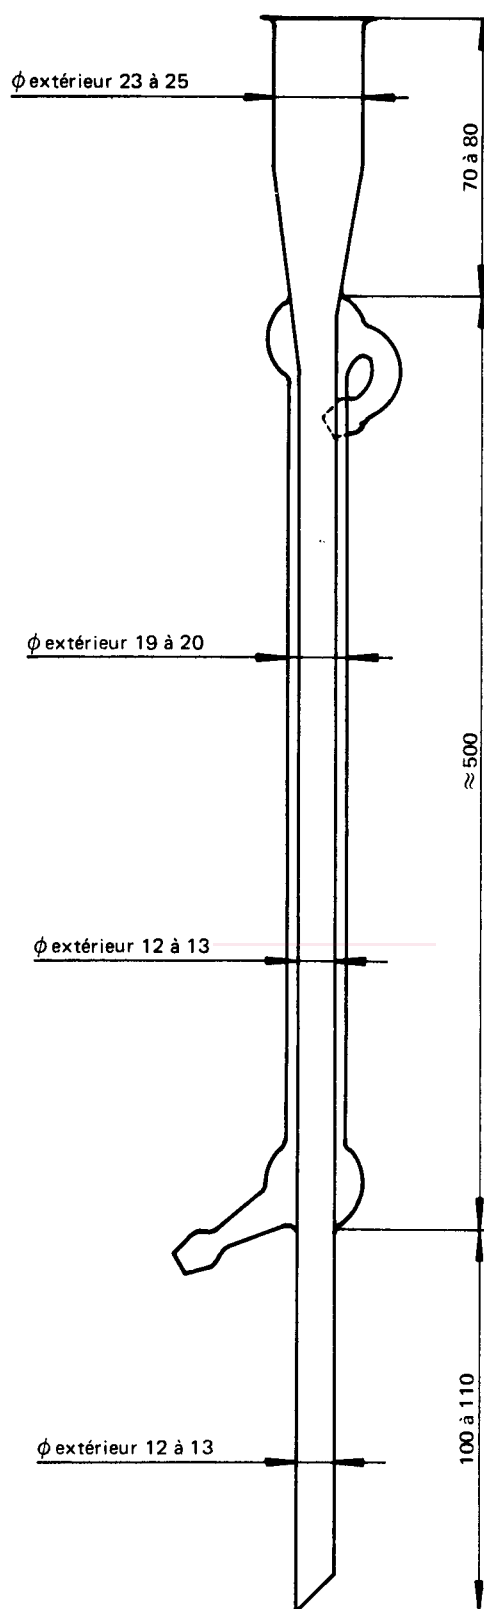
Réfrigérant de Liebig, entièrement en verre (D)
